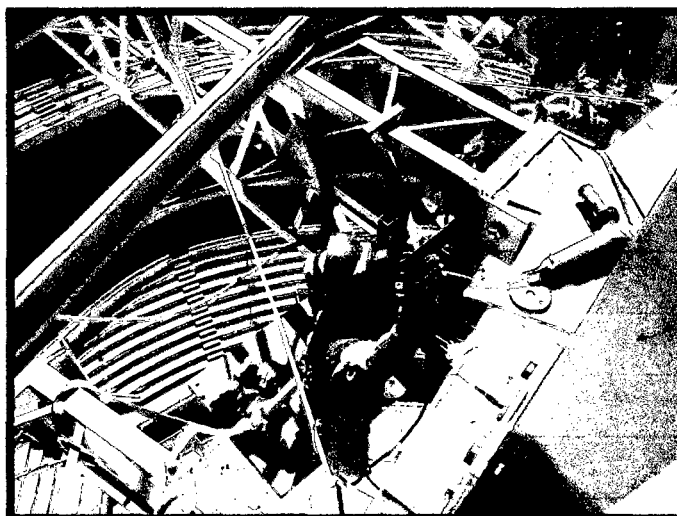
Se observa al soldador 6G realizando la rectificación de la soldadura.
